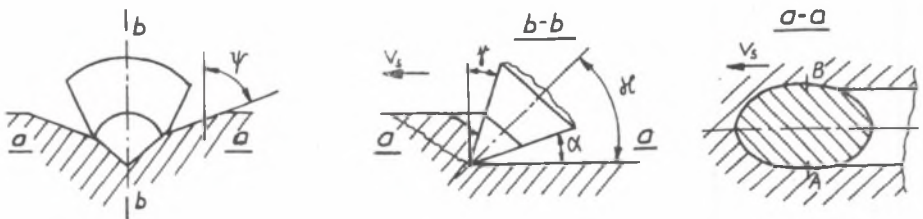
Przekrój skrawu uzyskiwanego nożem soczewkowym: 1 - główna krawędź skrawająca, 2 - boczna krawędź skrawająca, 3 - wyprzedzająca krawędź skrawająca
